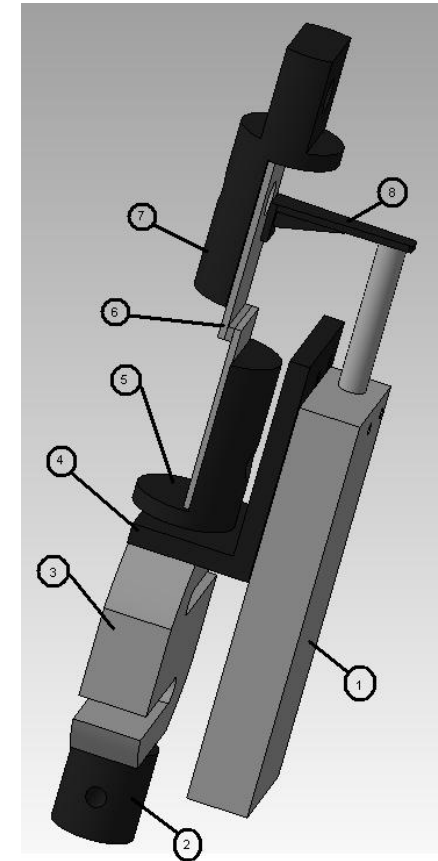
3D-модель сборки узла машины с датчиками и испытываемым образцом:
